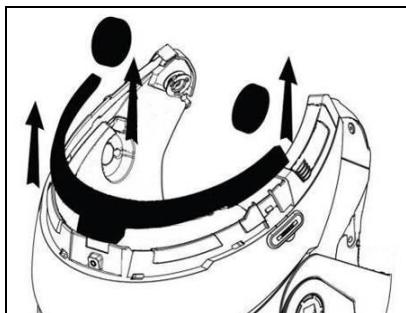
B - POUZE PRO PŘILBY N87, N80-8, N100-5
